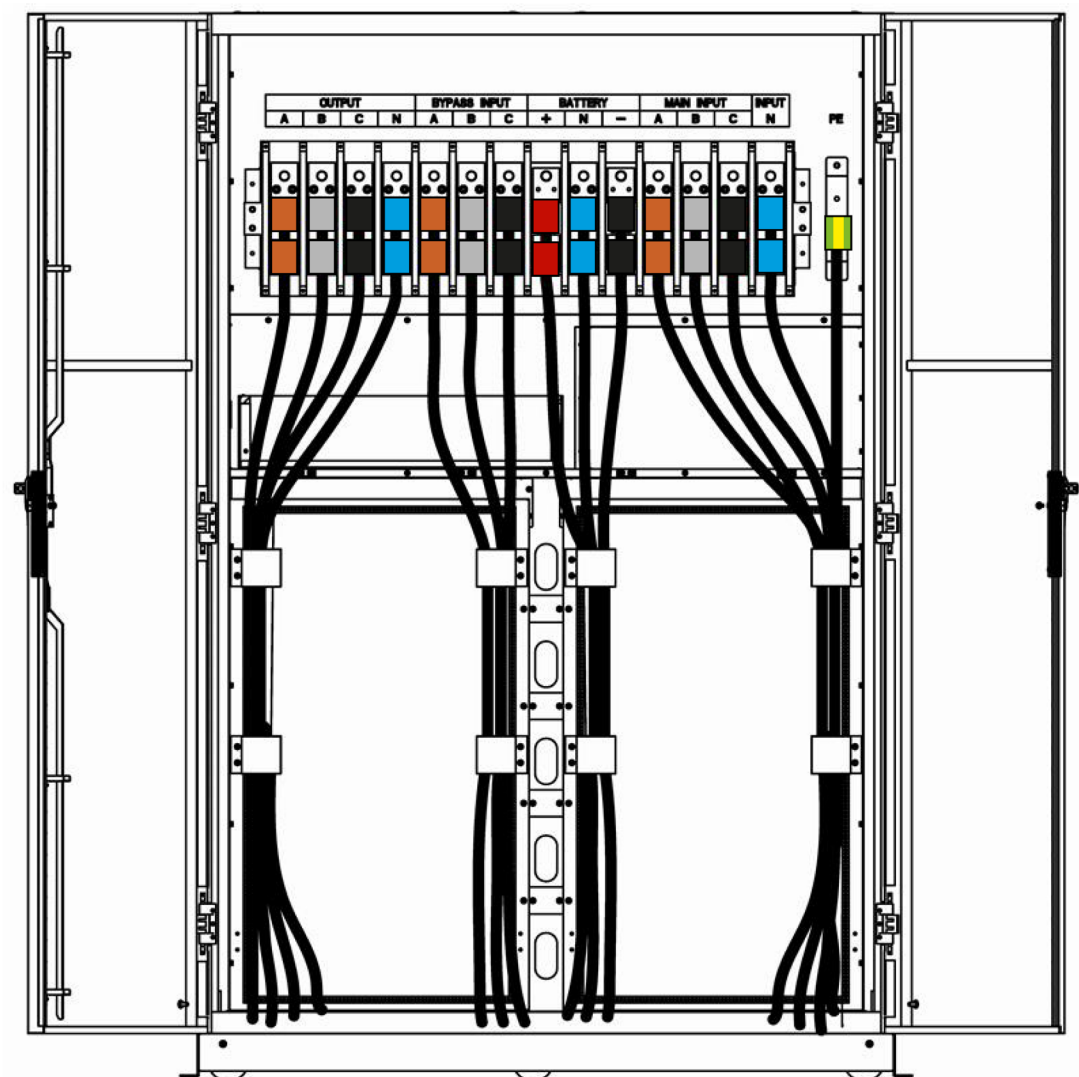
Entrada inferior de cables en armario de 10 slots.
